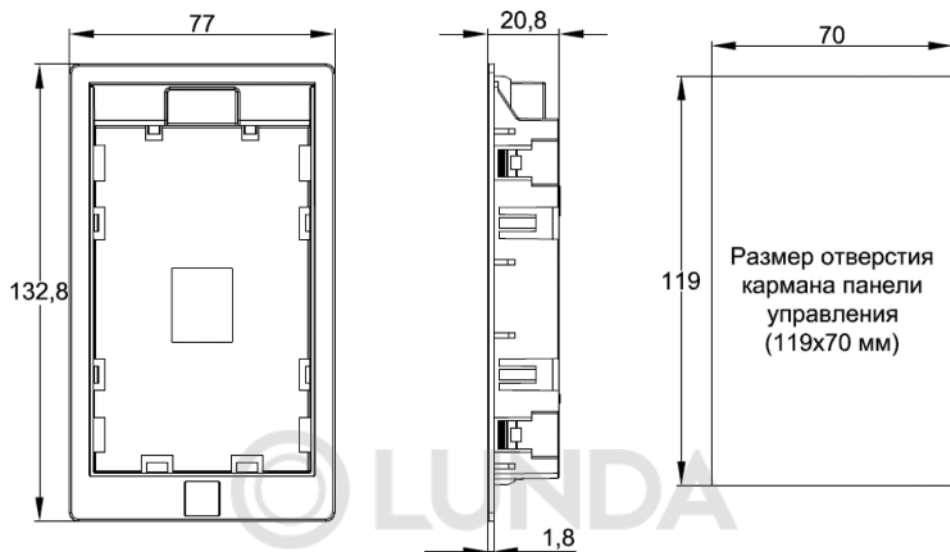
Габаритные размеры держателя внешней цифровой двухстрочной панели управления (единица измерения – мм)
